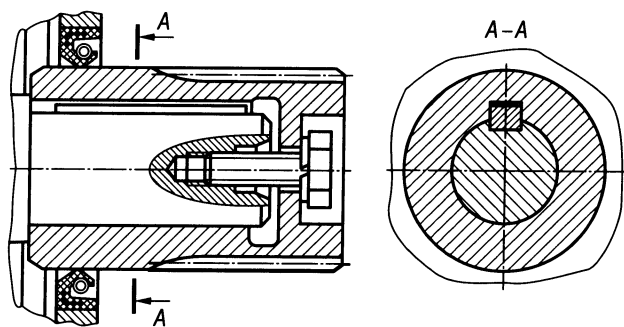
Шестерня цилиндрического зубчатого мотор-редуктора, установленная на валу электродвигателя
